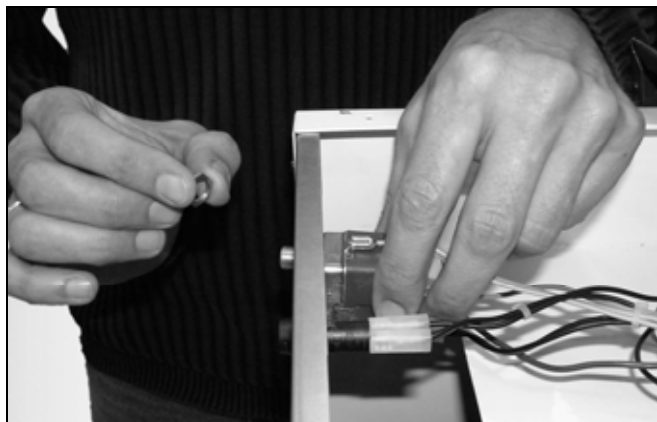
Die Befestigungsmutter des STB abschrauben, diesen von innen durch das Frontverkleidungsblech hindurch stecken und ihn dort von außen mit der Mutter festschrauben.
